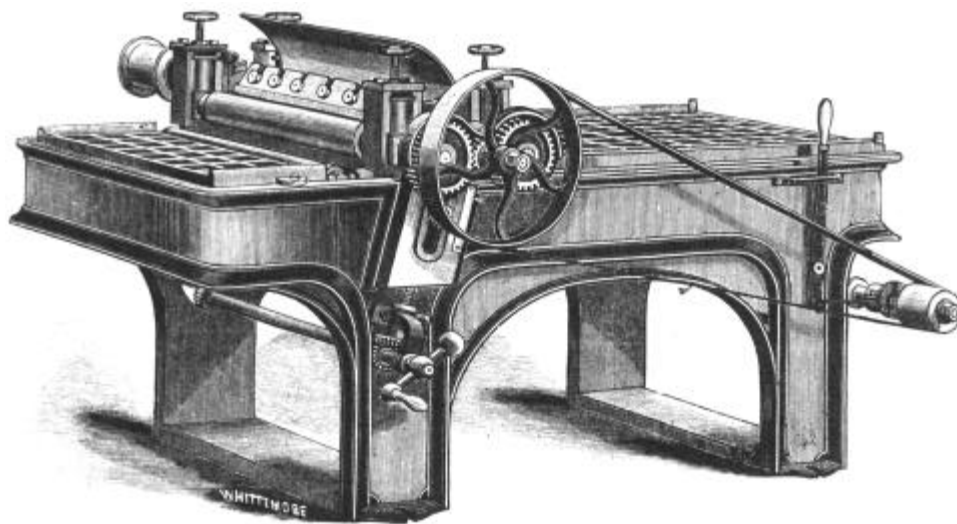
Woodworthsche Planhobelmaschine mit Gitterbett, Speisewalzen und in einem Oberlager angebrachter Messerwelle, 1873.
